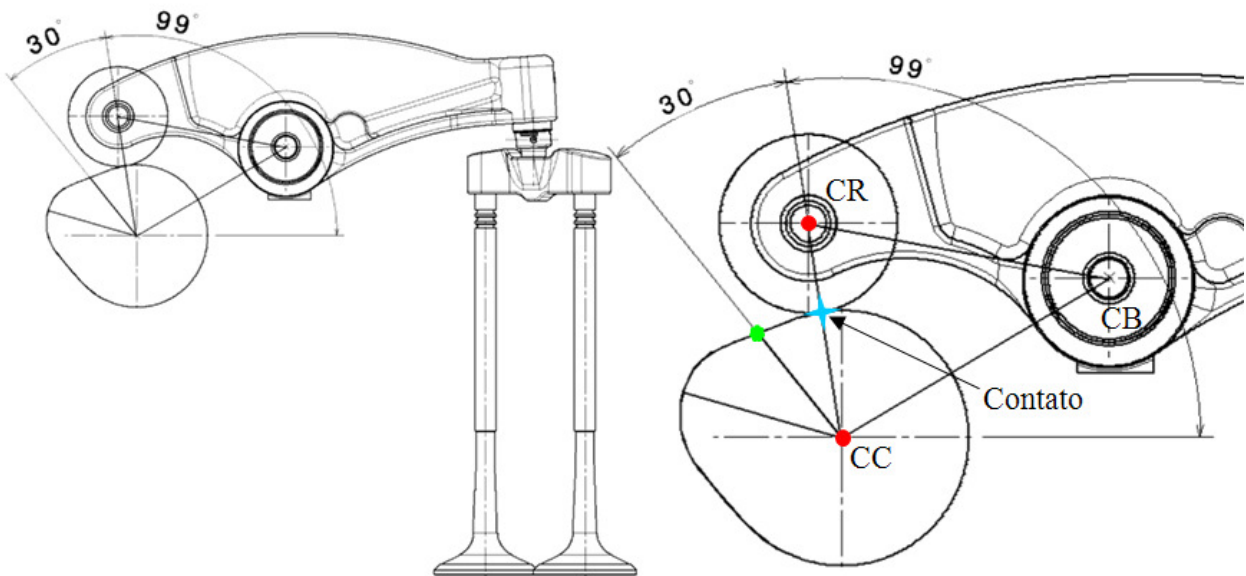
Came posicionado com o rolete no início do perfil do came.
